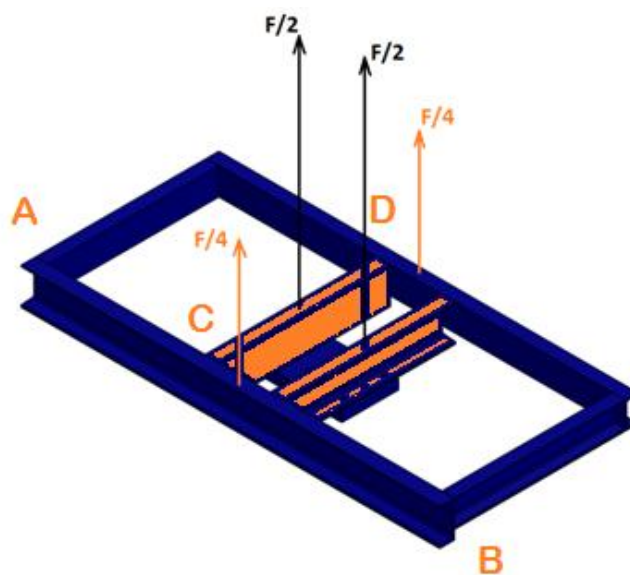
Distribución de fuerza en las vigas AB y CD.
